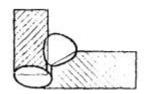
Соединение угловое со скосом одном кромки двустороннее (приварка плоских фланцев) У7
